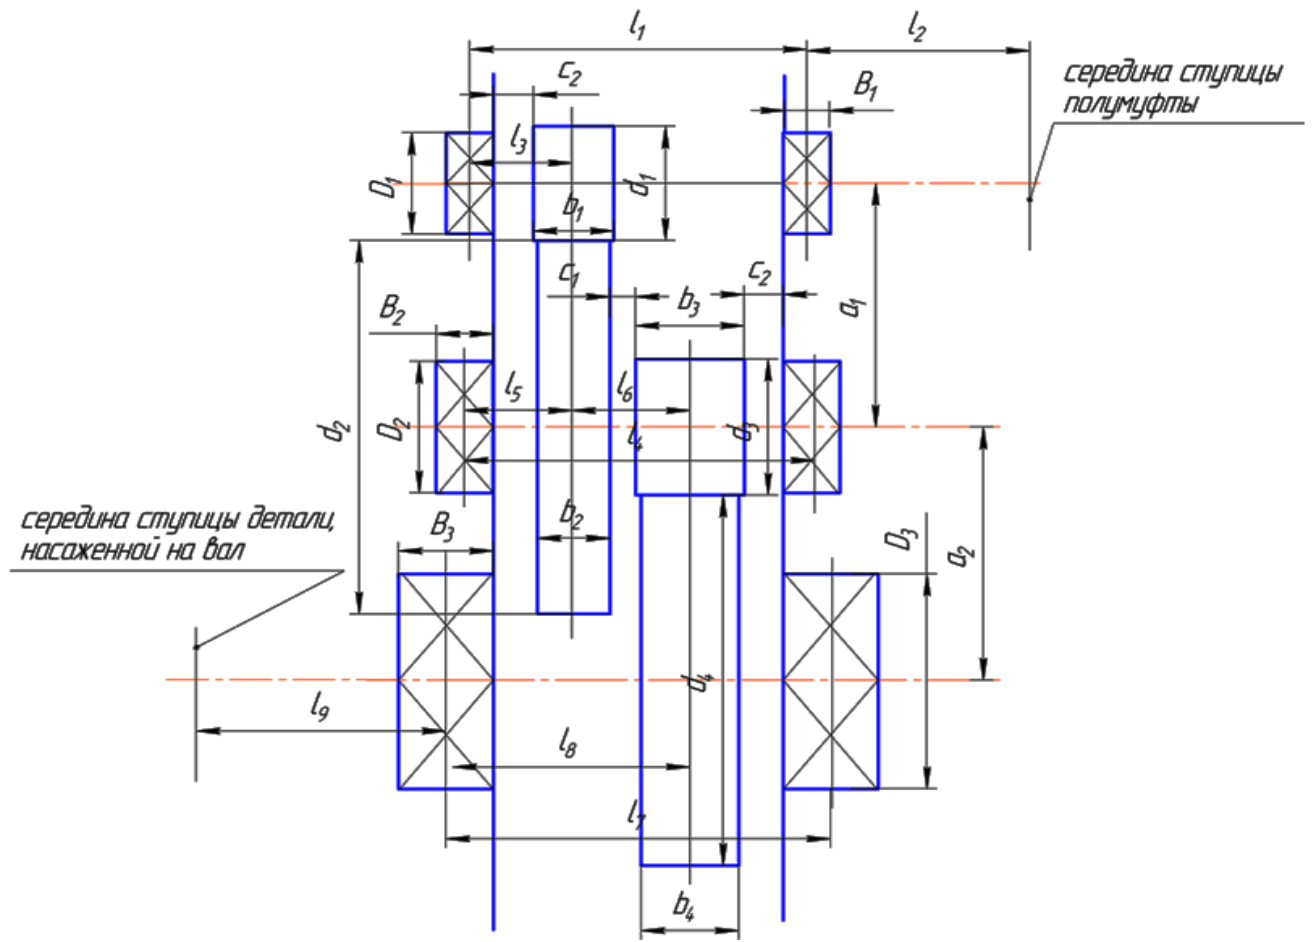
Компоновка двухступенчатого цилиндрического редуктора
